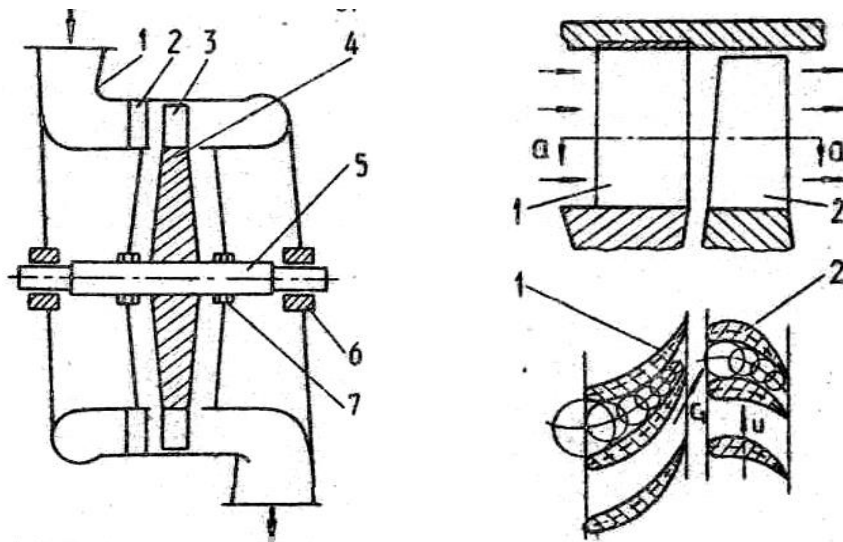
Газова осьова турбіна.1- вхідний направляючий апарат (канал);2- лопатки соплового апарату ; 3- лопатки робочого колеса; 4- робоче колесо турбіни; 5 – вал турбіни; 6- підшипники валу; 7- шпонки кріплення робочого колеса.
